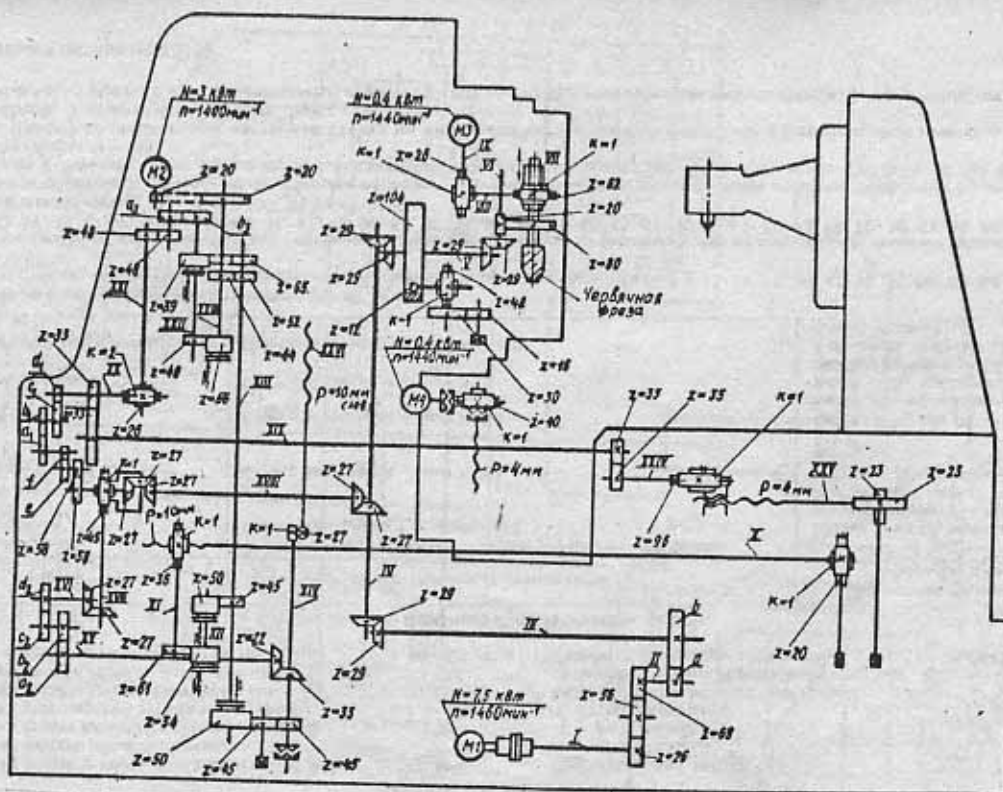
Кинематическая схема зубофрезерного полуавтомата мод. 5М324А
